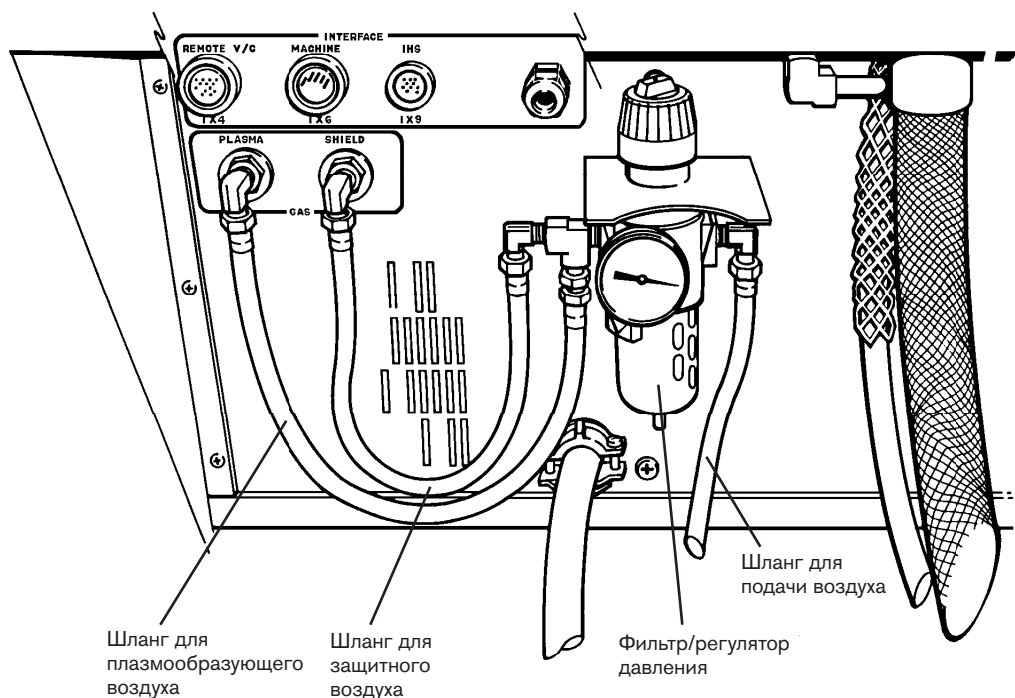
Подсоединения плазмообразующего и защитного воздуха
